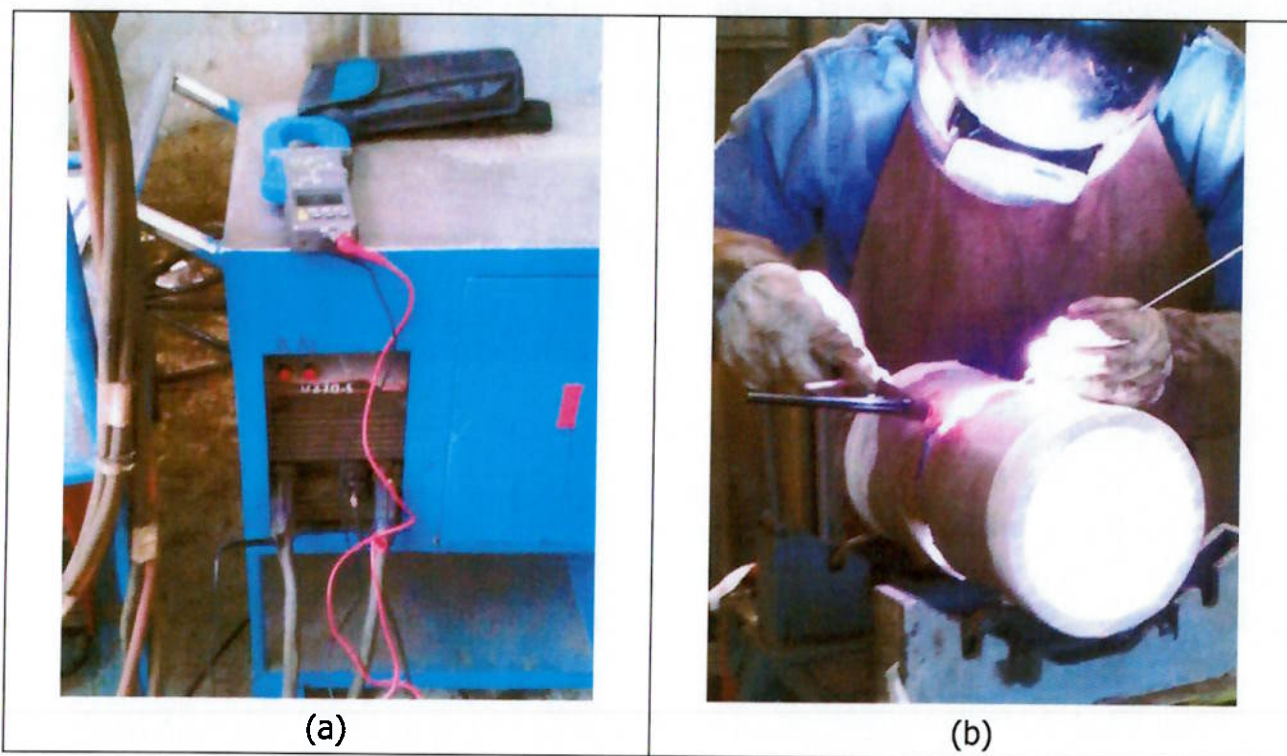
(a) Ajuste e Medição dos Parâmetros na Máquina de Solda. (b) Execução da Raiz da Solda - TIG.
